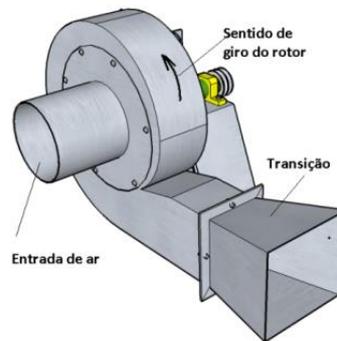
Vista final do ventilador, com detalhe do eixo e sentido de giro para eixo comum.
